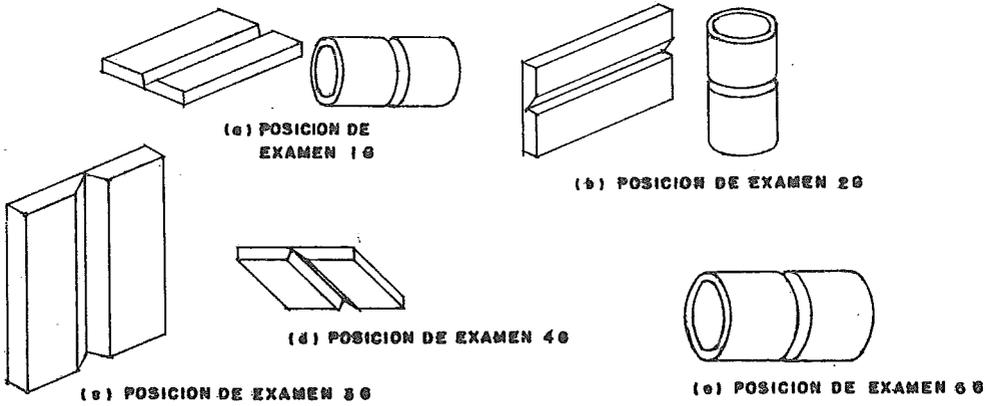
POSICIONES DE PLACAS Y TUBOS A EXAMINAR PARA SOLDEO EN RANURA
